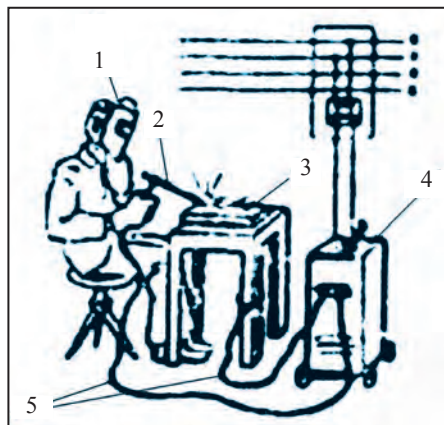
Оборудование для электросварки: 1 – защитная шлем маска; 2 – электрод; 3 – деталь; 4 – сварочный аппарат; 5 – провода.
